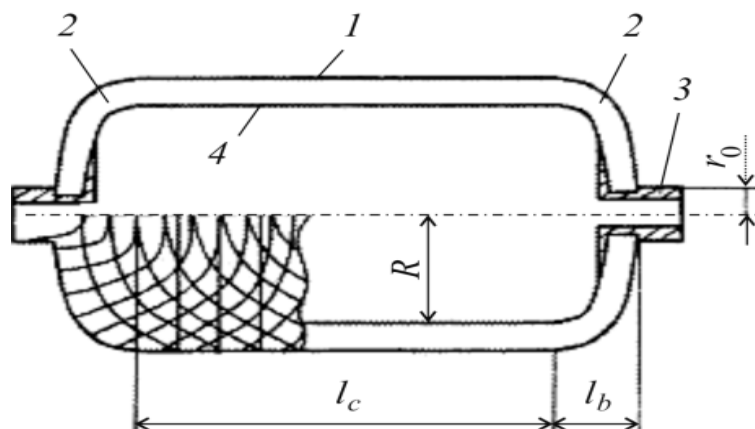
Типова схема композитного балона високого тиску: 1 – циліндрична частина; 2 – днище; 3 – закладні елементи; 4 – полімерний лейнер
